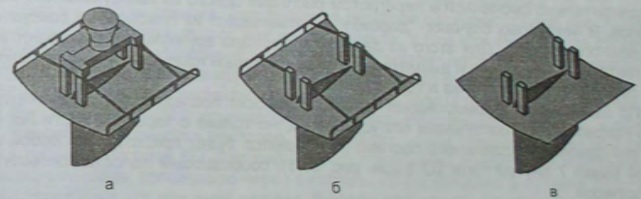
Схемы этапов удаления элементов ЛПС с отливки
